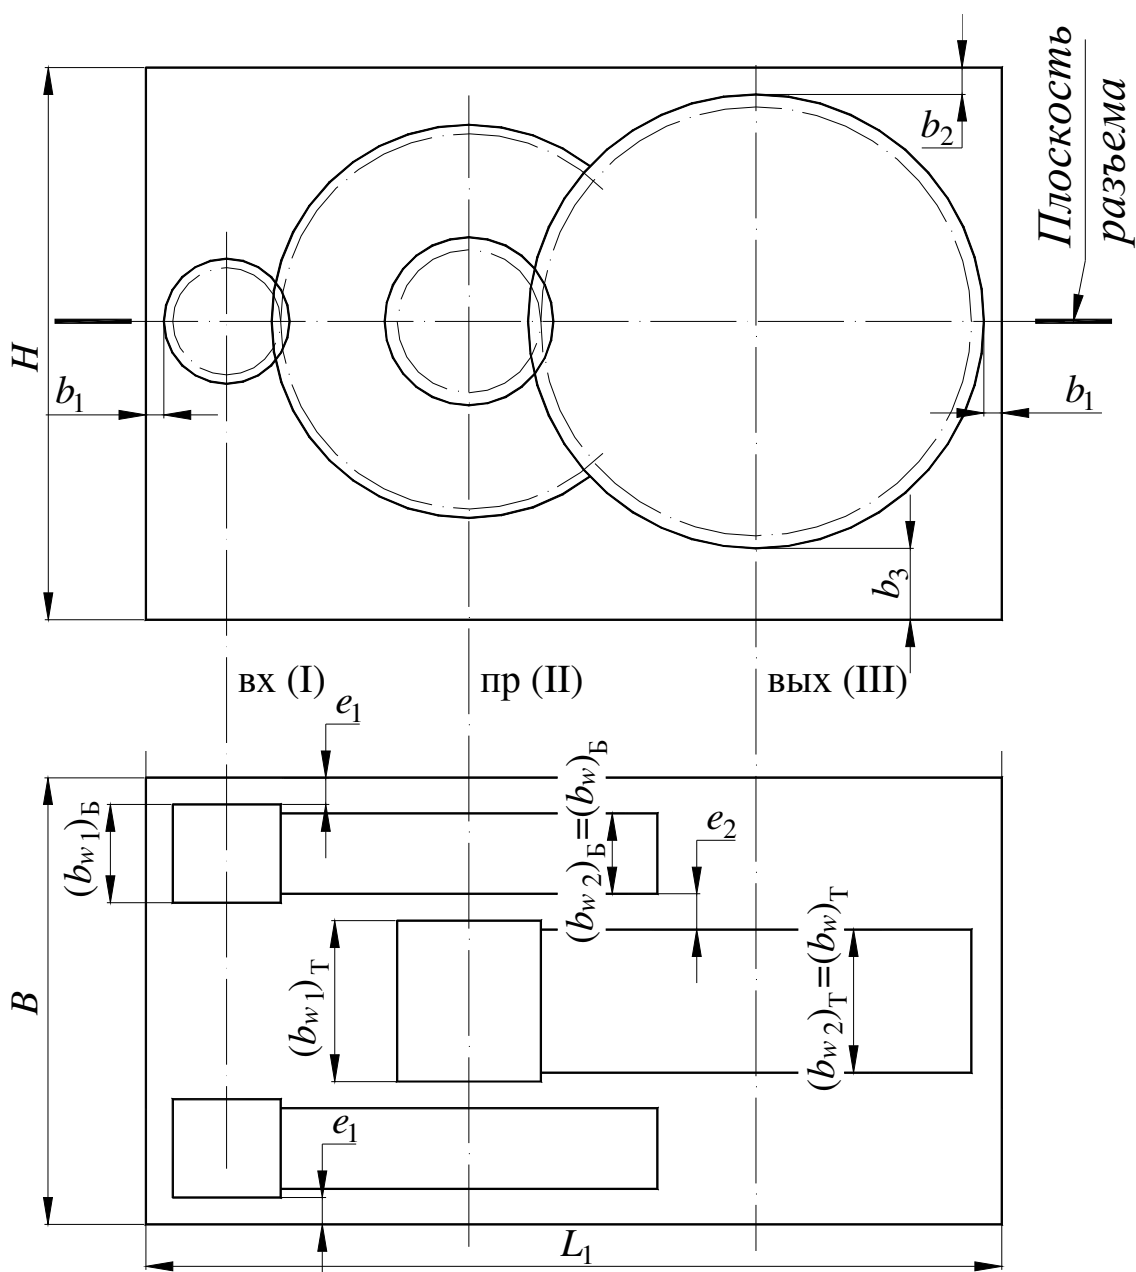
Первый этап эскизной компоновки двухступенчатого цилиндрического редуктора по схеме раздвоенный шеврон
